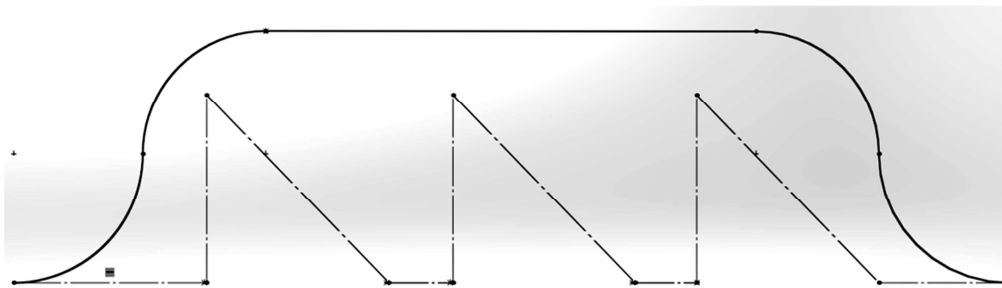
Розгортка поковки з розмірами (вигляд збоку)
